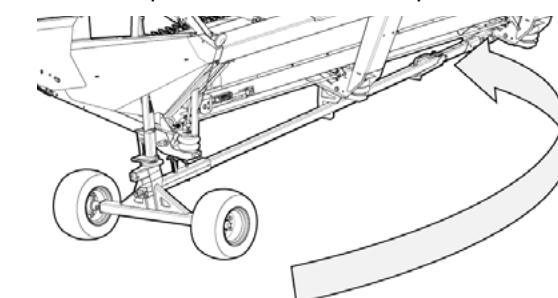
Поворот сцепного стержня в положение для хранения.
